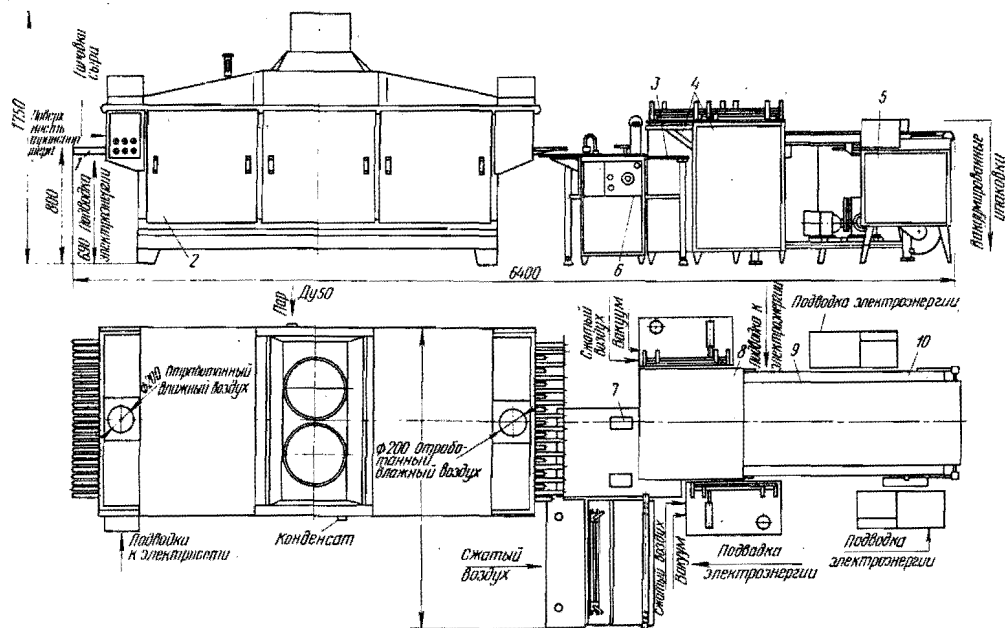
Общий вид линии марки М6-ОЛА для упаковки сыров в полимерную пленку на период созревания:
